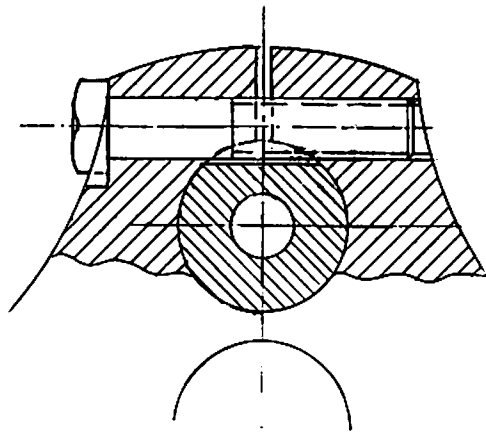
Befestigung des Kurbelzapfens durch Klemmung mittels Schraube.
